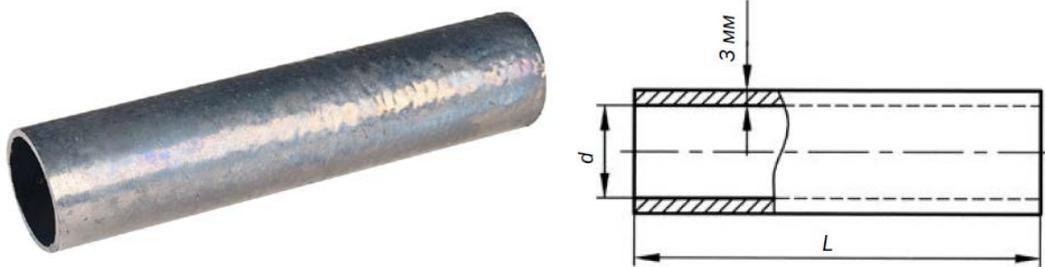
Внешний вид свинцовой муфты типа «труба» и рисунок с размерами.
